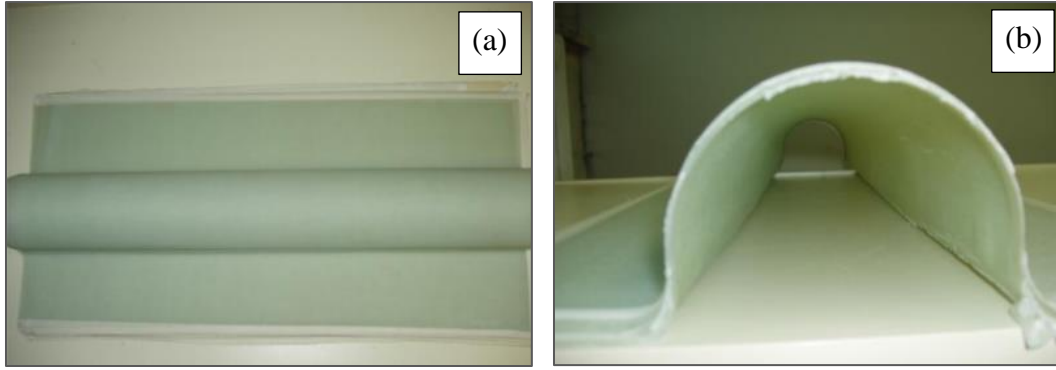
Coque infusée : a) vue de côté et b) vue de face
